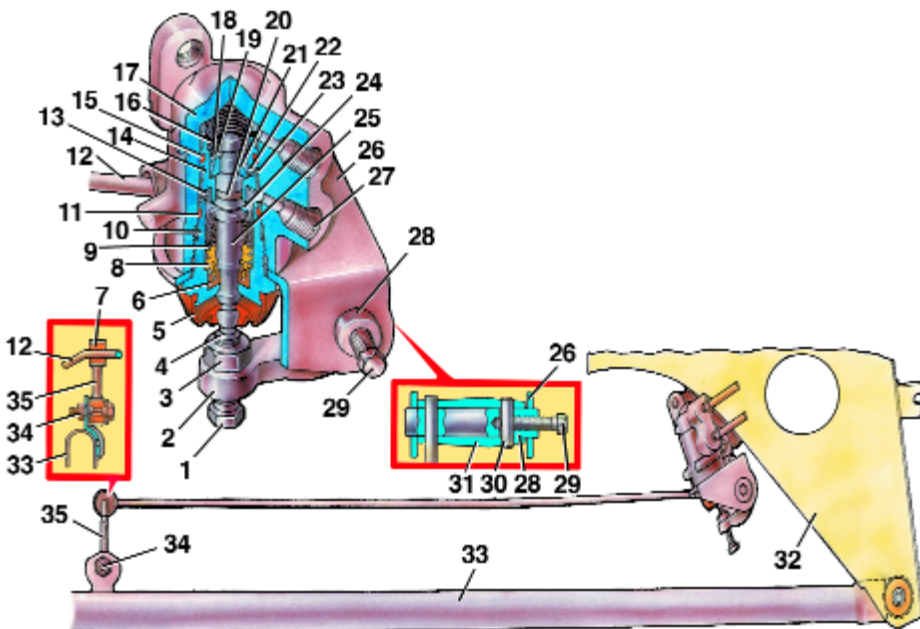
Регулятор давления: 1 – регулировочный болт; 2 – нажимной рычаг; 3 – контргайка; 4 – шайба; 5 – грязезащитный чехол; 6 – уплотнительная манжета; 7 – втулка стойки; 8 – распорная втулка манжеты малой ступени поршня; 9 – возвратная пружина; 10 – втулка крепления корпуса; 11 – уплотнительное кольцо втулки; 12 – нагрузочный стержень; 13 – пружинная шайба; 14 – гильза поршня; 15 – уплотнительное кольцо гильзы; 16 – прижимная пружина конуса; 17 – корпус; 18 – промежуточная шайба; 19 – стопорная шайба; 20 – уплотнительная манжета большой ступени поршня; 21 – конус; 22 – шариковый клапан; 23 – прижимная пружина шарика; 24 – скоба; 25 – поршень; 26 – кронштейн; 27 – гнездо для подвода жидкости; 28 – ось нажимного рычага; 29 – болт; 30 – штифт; 31 – ступица нажимного рычага; 32 – кронштейн поперечной штанги; 33 – поперечная штанга; 34 – ось стойки; 35 – стойка
